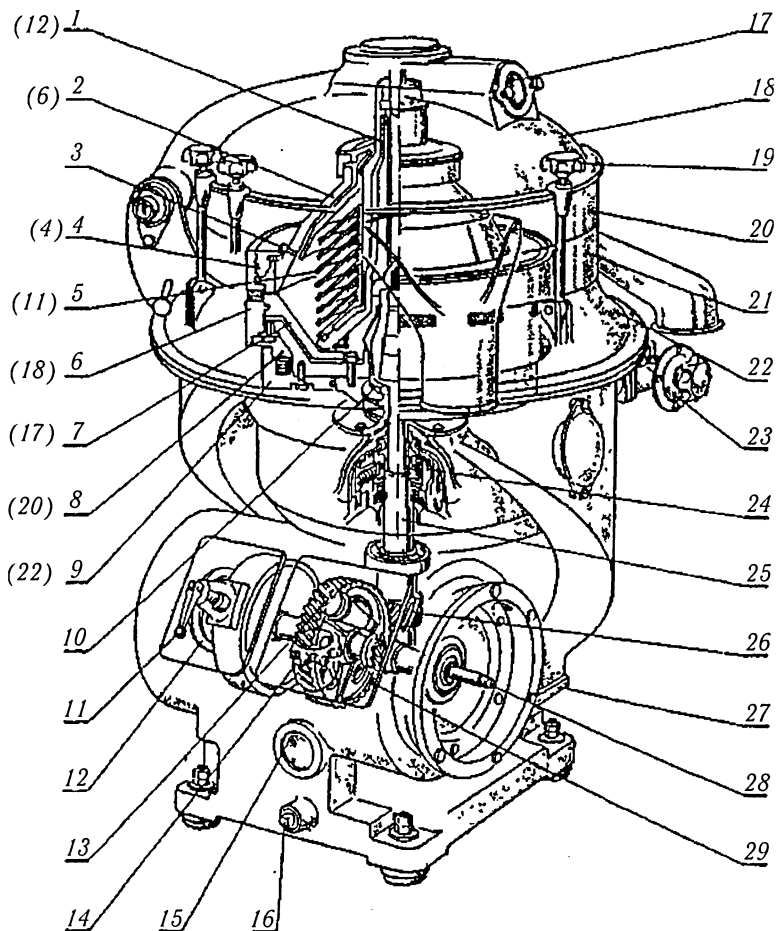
Общий вид сепаратора МАРХ309В-00: 1 — тарелкодержатель; 2 — крышка барабана; 3 — винт; 4 — большая кольцевая гайка; 5 — пакет тарелок барабана; 6 — барабан; 7 — передвигное дно барабана; 8 — кольцо управляющее; 9 — корпус пружин; 10 — распределительное устройство; 11 — тормоз; 12 — фрикционная муфта; 13 — тахометр; 14 — пробка заливной горловины; 15 — указатель уровня масла; 16 — пробка сливной горловины масла; 17 — смотровое окошко; 18 — крышка сборника; 19 — крепежный болт крышки сборника; 20 — верхний сборник; 21 — нижний сборник; 22 — корпус; 23 — кран управления; 24 — верхняя опора вертикального вала; 25 — вал барабана; 26 — червяк вертикального вала; 27 — патрубок спуска шлама; 28 — горизонтальный вал; 29 — червячное колесо
